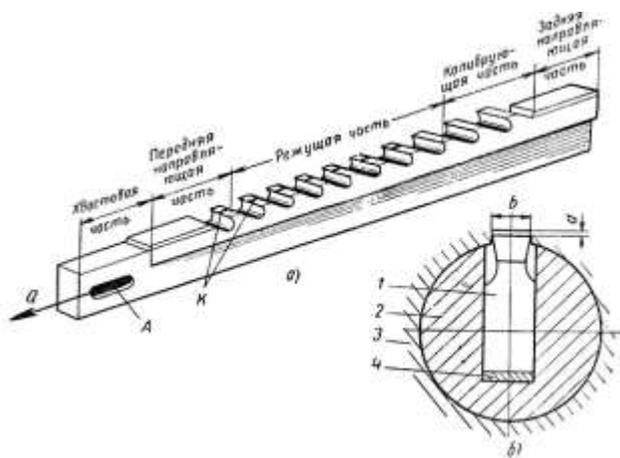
Схема протягивания шпоночного паза: а - шпоночная протяжка; б - схема резания: 1 - протяжка; 2 - направляющая втулка; 3 - заготовка; 4 – прокладка
